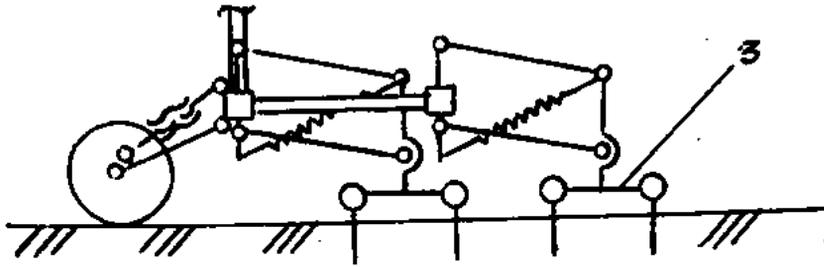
Схема орудий для поверхностной обработки почвы: 1 - рама; 2 - параллелограммный механизм; 3 - рыхлитель; 4 - опорное колесо
